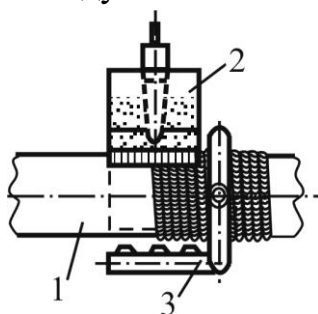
Схема вибродуговой наплавки под флюсом
